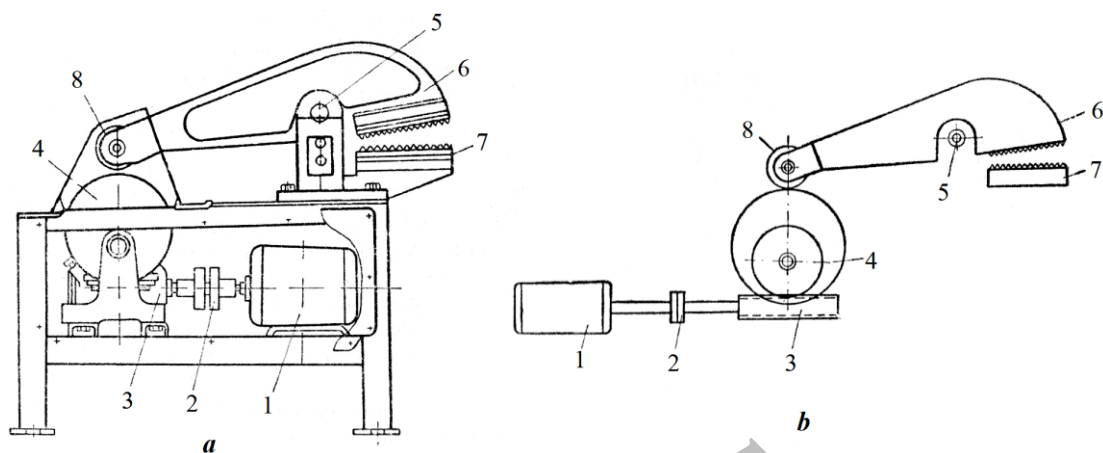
Schema unei mașini de dezongulat picioare de bovine: a- schema mașinii; b- schema cinematică de acționare: 1- electromotor; 2- cuplaj elastic; 3- reductor melcat; 4- excentric; 5- ax de balansare; 6- falcă mobilă; 7- falcă fixă; 8- rolă presare cu excentric
